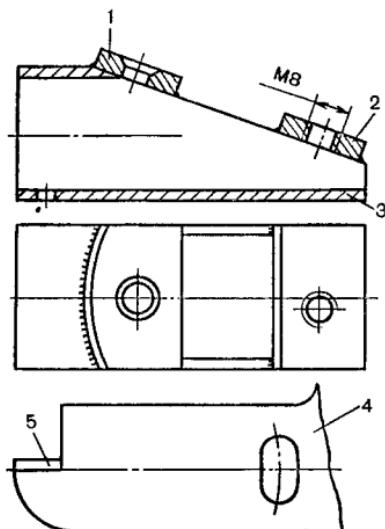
Устройство для крепления ножа и регулирования захвата косы:
